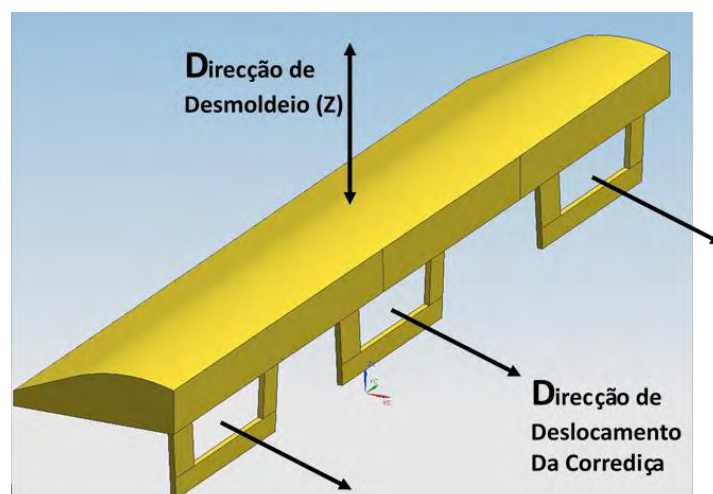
Representação de uma peça com Indicação das direções de desmoldagem
